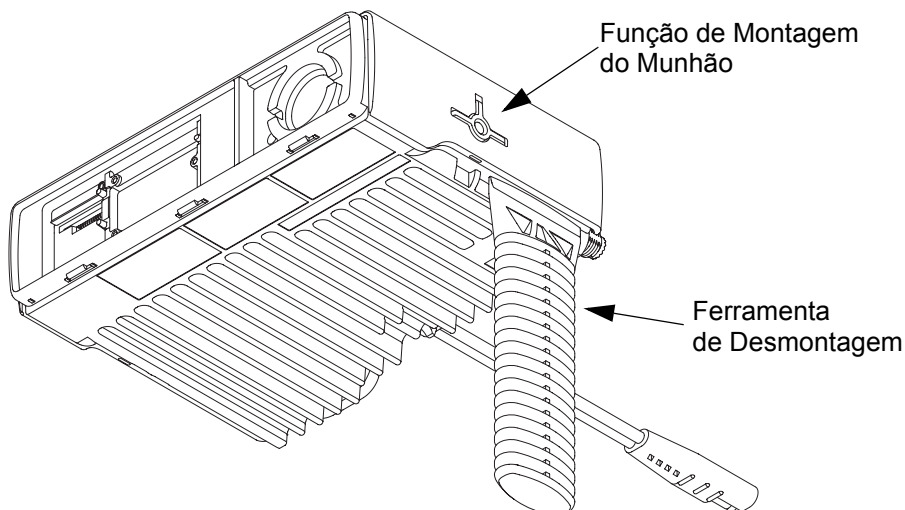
Remoção da Tampa Superior (A Imagem Pode Não Ser Exatamente Igual Ao Produto)
